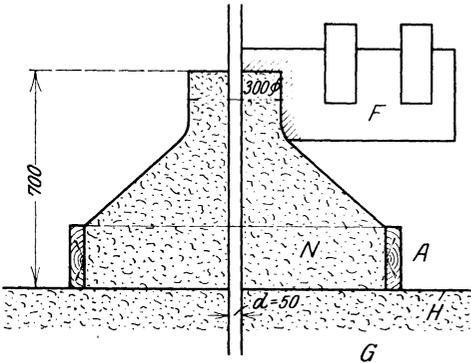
Schwenkschablone zum Schablonieren des oberen Durchmessers.
